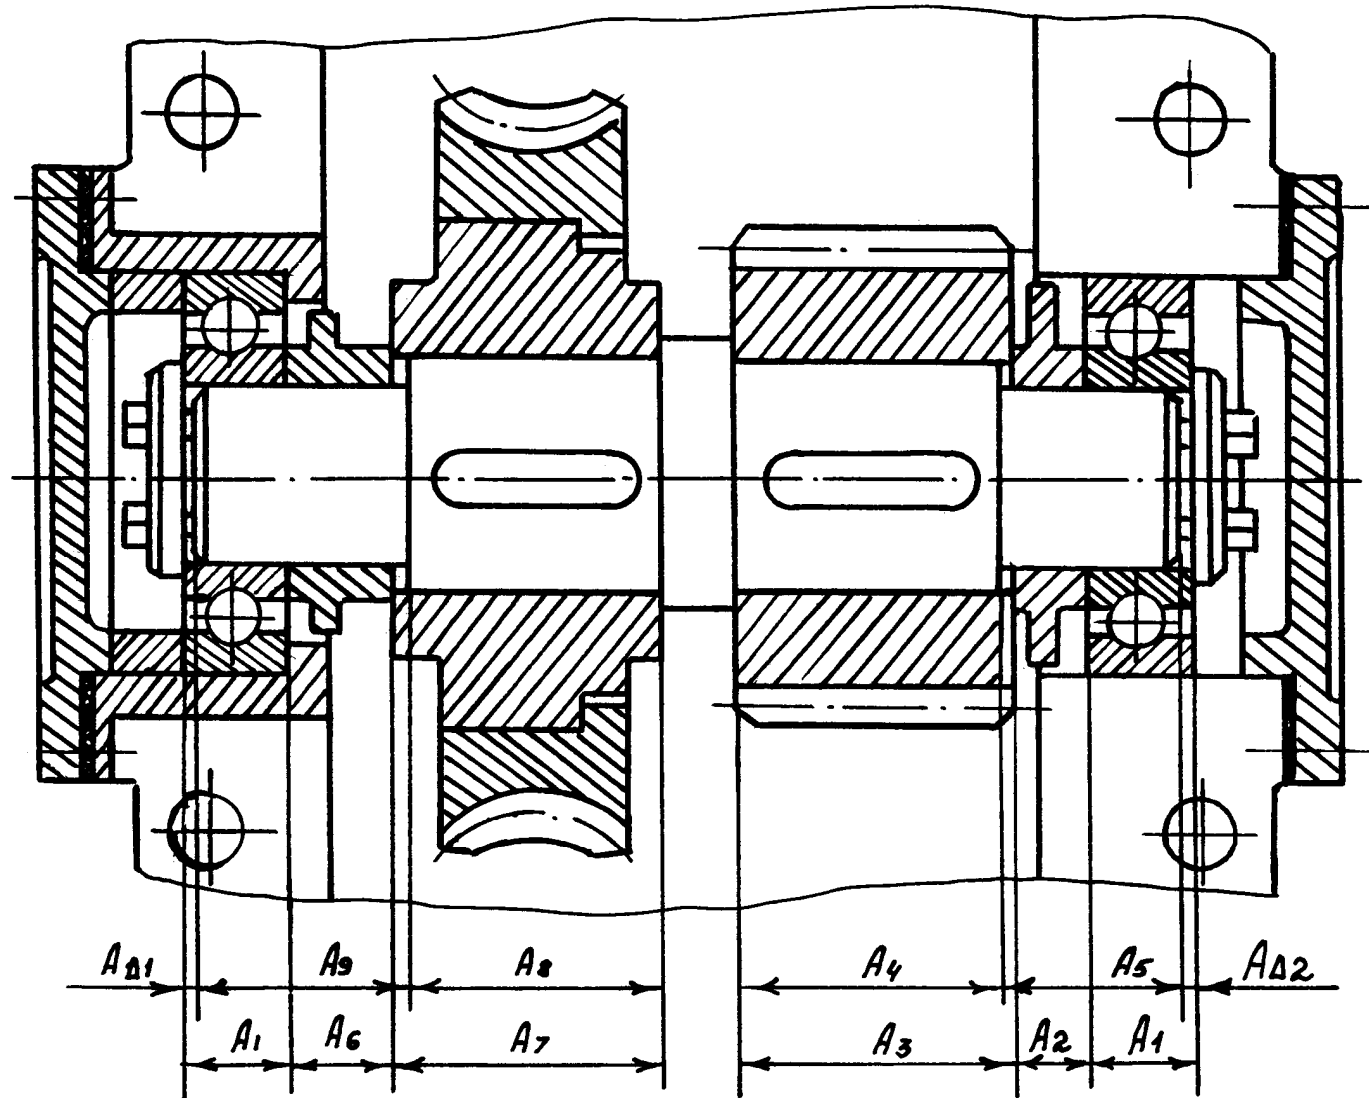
Эскиз узла промежуточного вала червячно-цилиндрического редуктора
